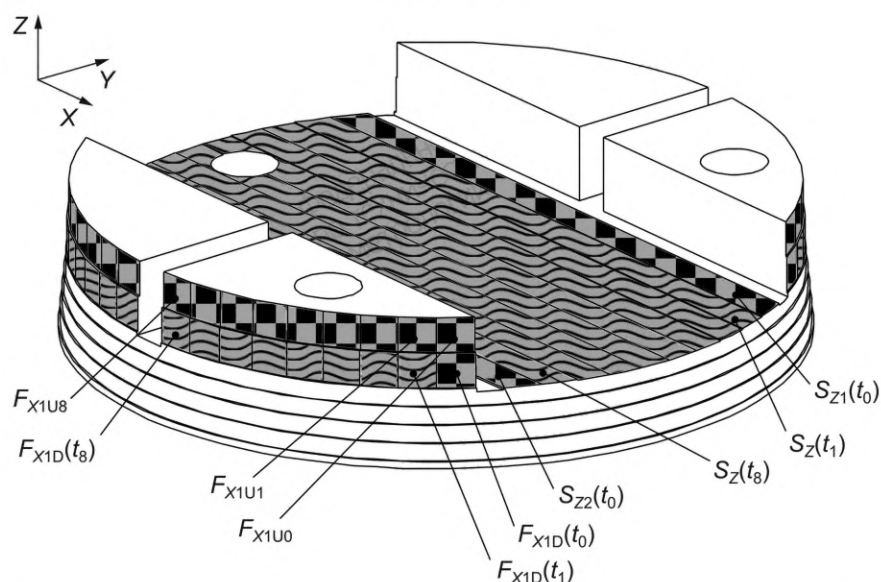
Геометрические размеры готового испытуемого образца с выделенными базовой (шахматная штриховка) и измерительными поверхностями (волновая штриховка)
